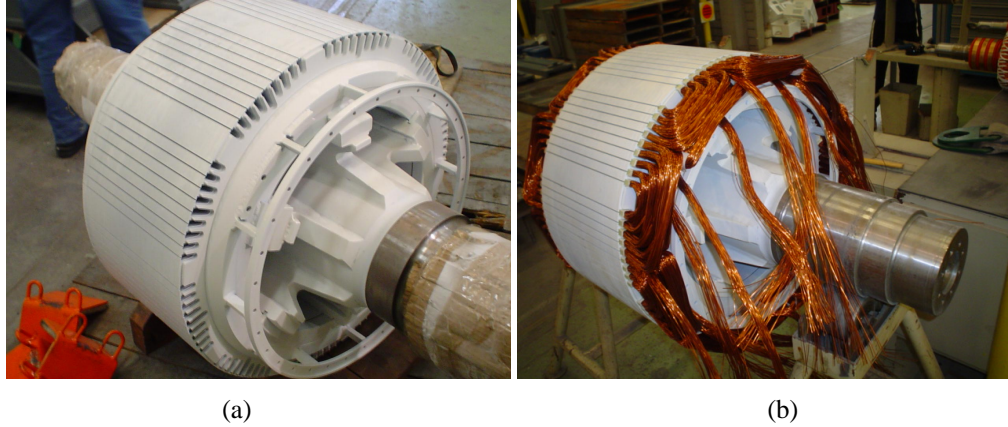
(a) Pacote de chapas do rotor, (b) Bobinas do rotor.
